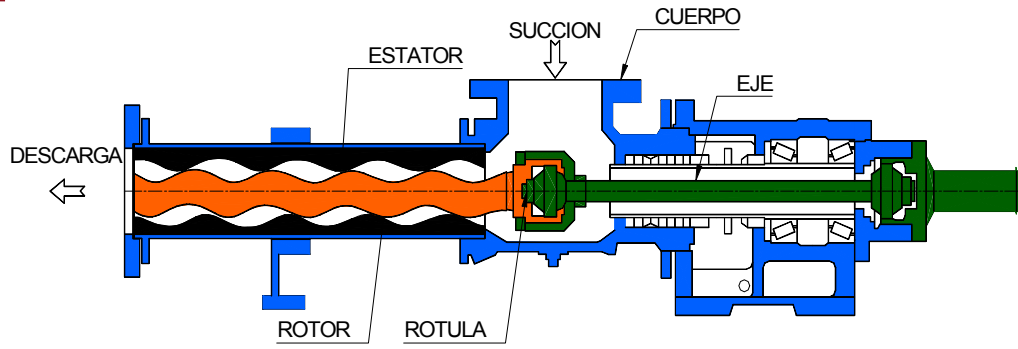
Partes componentes de Bomba de cavidad positiva.
